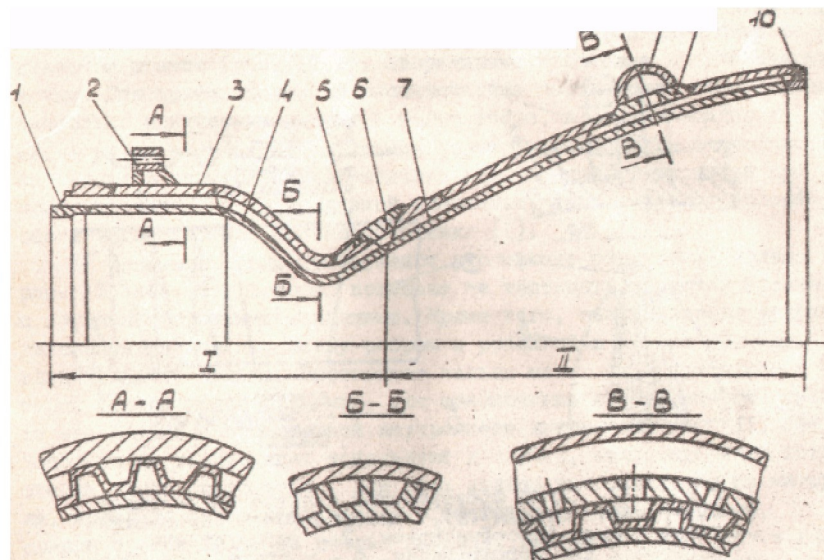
Схема корпуса паяно-сварной камеры:
